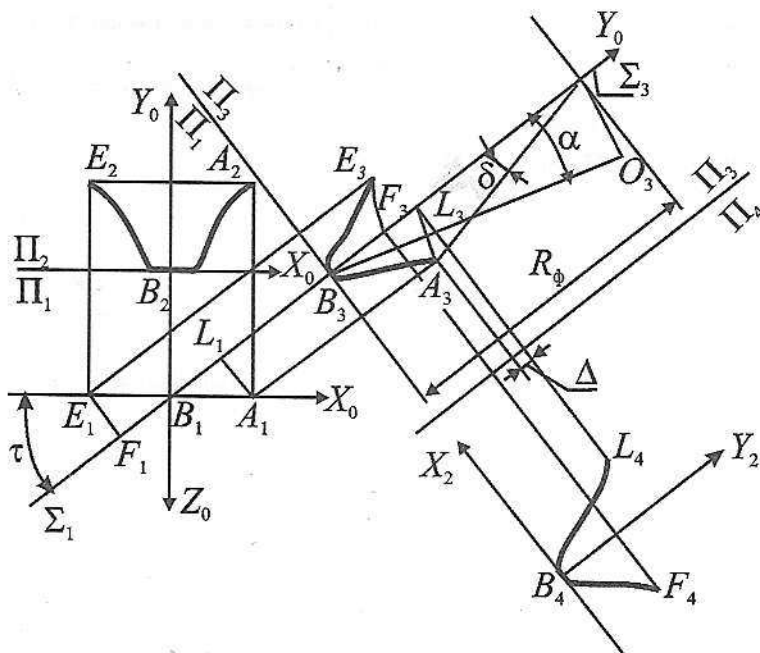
Схема образования задней поверхности обкаточной фрезы
